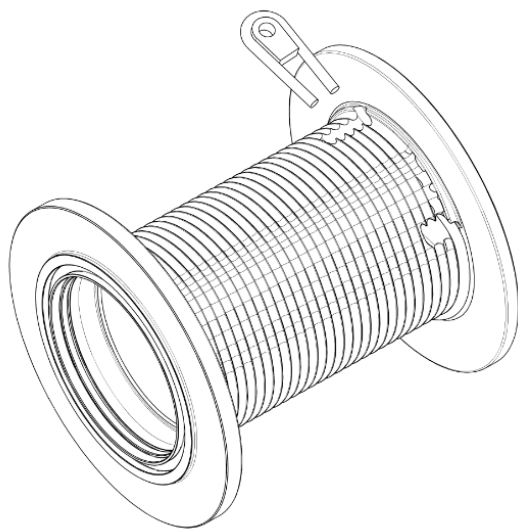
Insira o cabo na fenda da flange do tambor e verifique a direção da rotação do guincho, aperte o parafuso com o torque definido.
